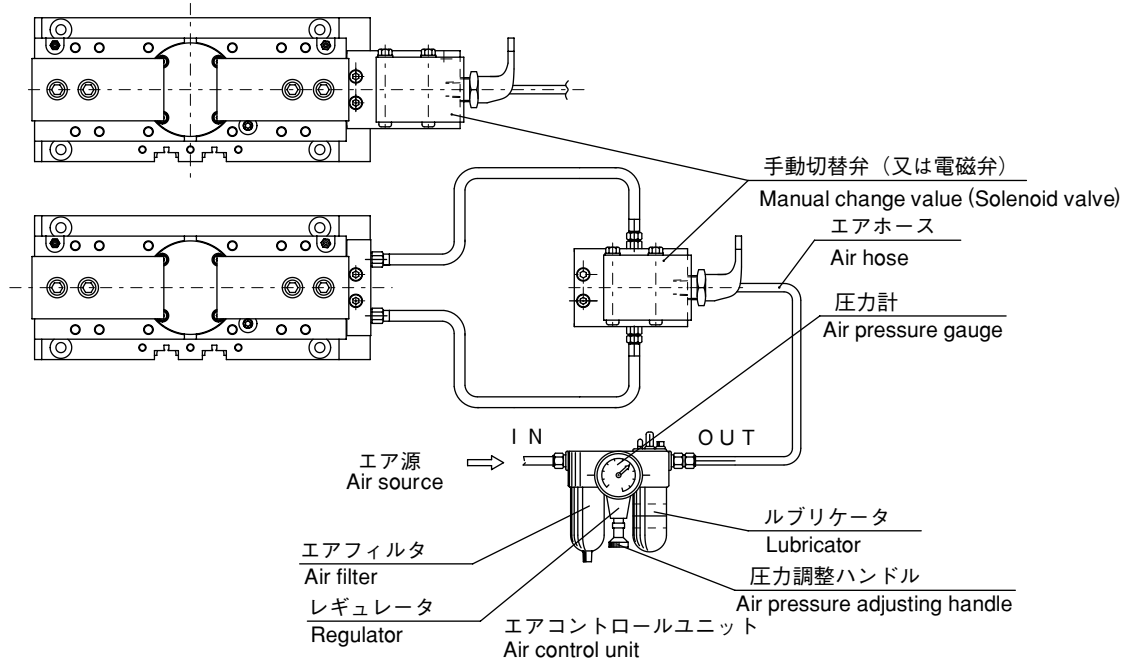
治具モジュール配管図 Piping drawing of Jig Module
